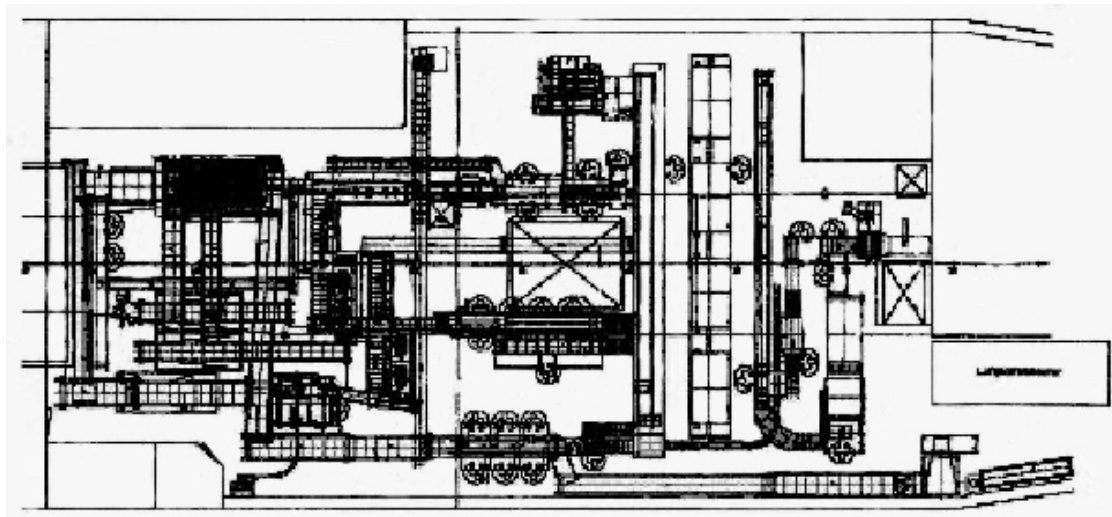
Схема общего расположения рыбообрабатывающего цеха
